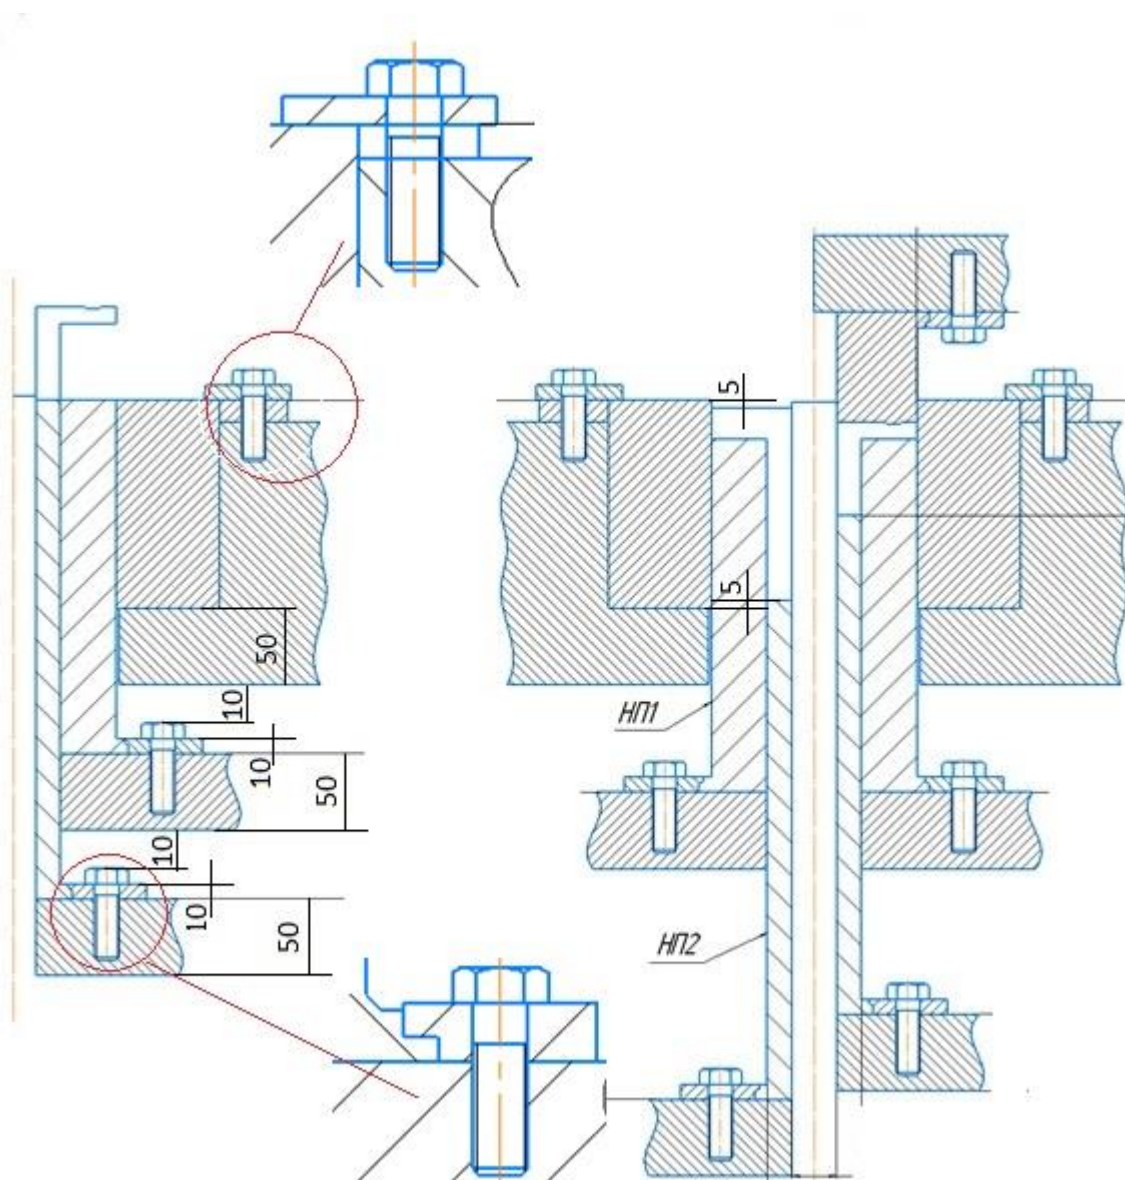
Схема для определения основных размеров сменных элементов пресс-формы для внешнего фланца.
